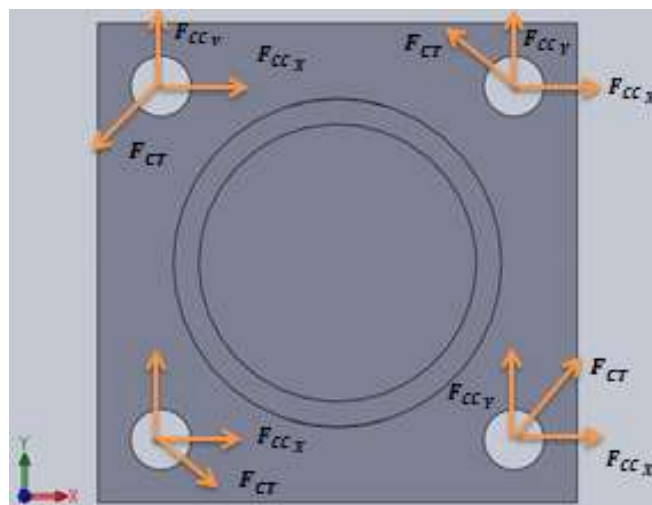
Conjunto de solicitaciones de corte sobre los tornillos
